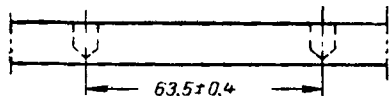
Сверление теплоотвода для монтажа вентильной конструкции с плоским основанием корпуса.
